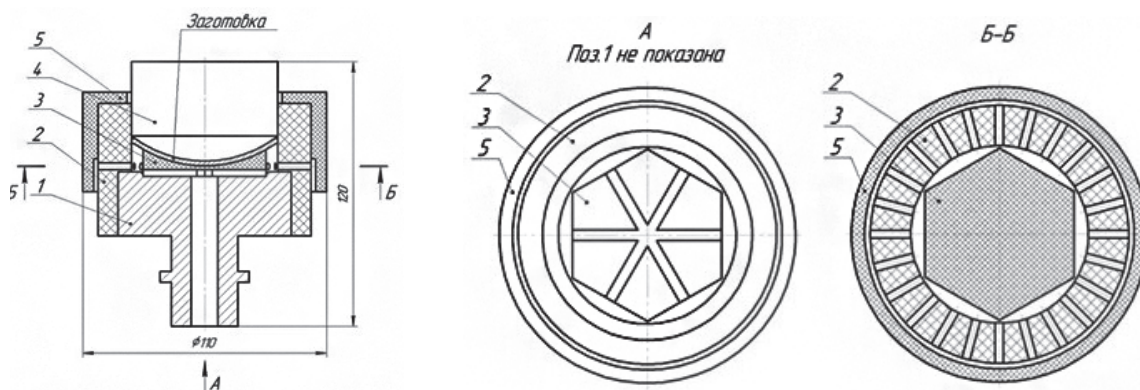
Схема приспособления для ЭХО менисковой облицовки:
